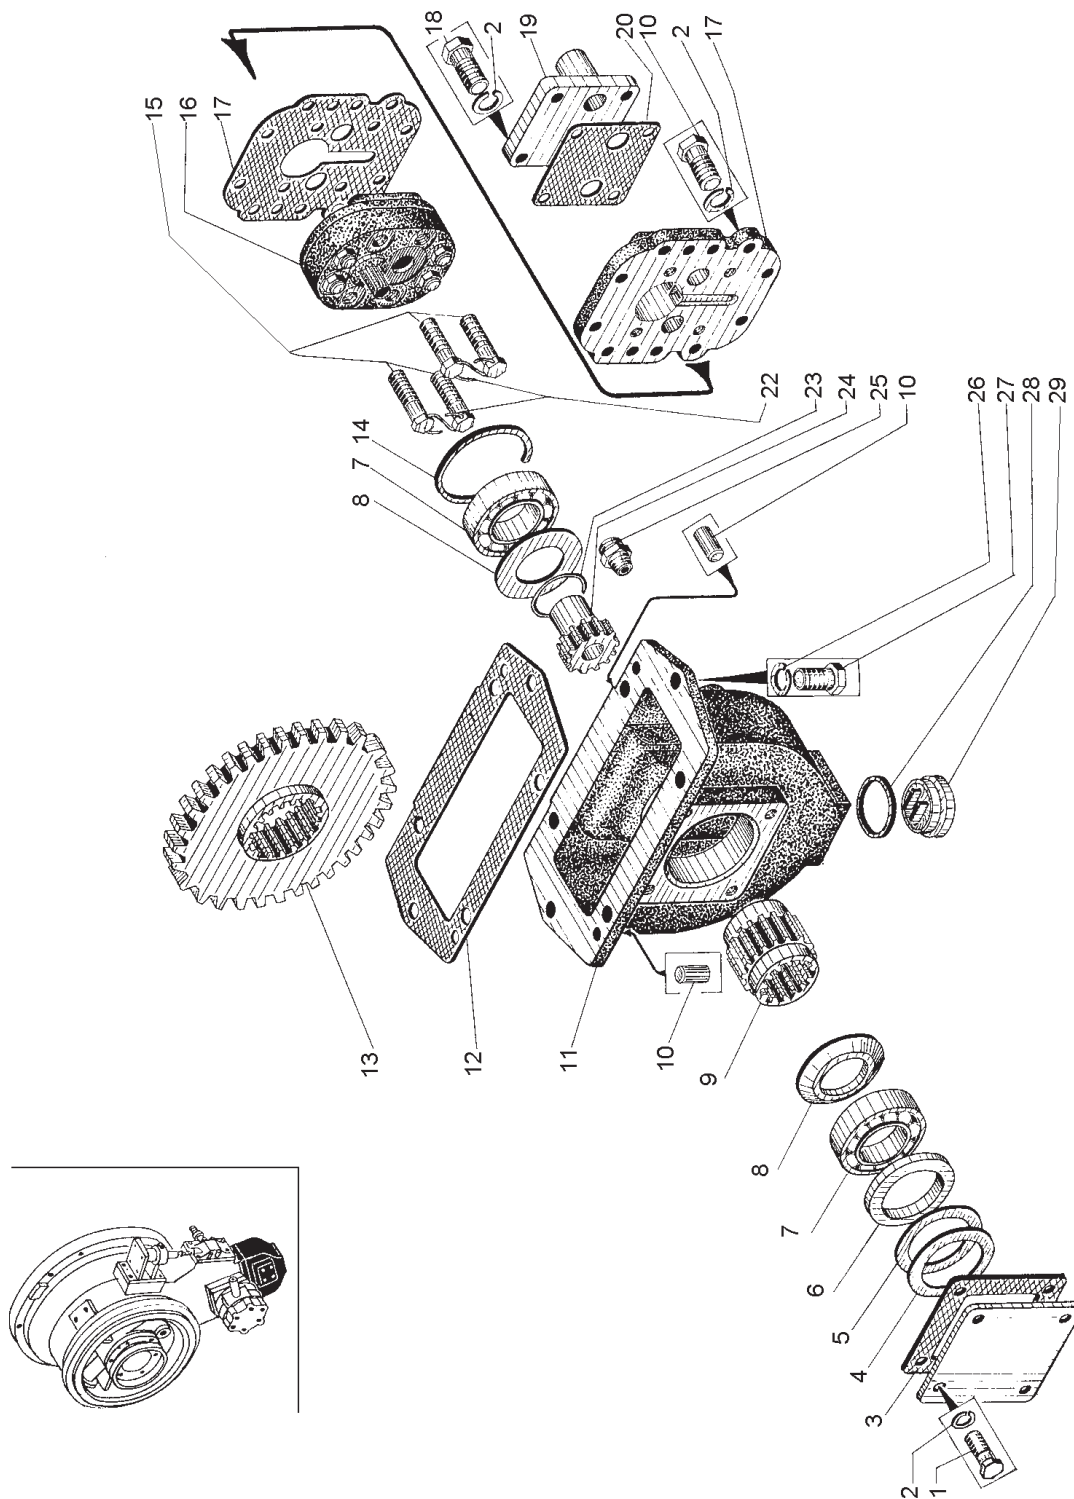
Редуктор промежуточный (ДЗ-98.10.06.000-09)
